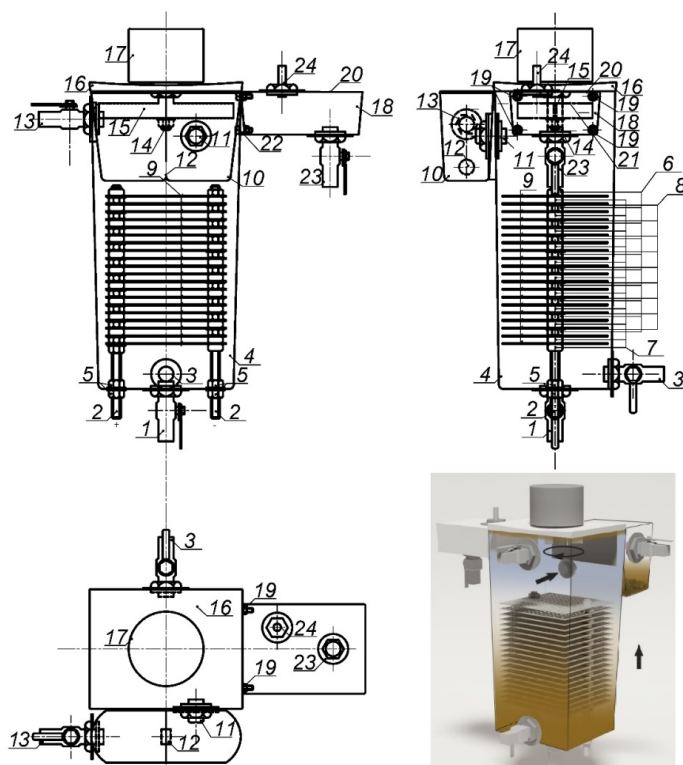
Электролизер-адсорбер для очистки СВ ТФ: 1 — кран для промывки устройства; 2 — направляющие контактные шпильки; 3 — штуцер подачи СВ; 4 — корпус устройства; 5 — гайки крепления контактных направляющих шпилек в корпусе установки; 6 — контактные гайки крепления пластин электродов; 7 — диэлектрические гайки крепления пластин электродов; 8 — диэлектрические прокладки; 9 — пластины электродов электролизера; 10 — адсорбер; 11 — штуцер для подачи в адсорбер СВ, прошедшей электрохимическую обработку; 12 — переливное отверстие адсорбера; 13 — кран слива очищенной воды; 14 — вал скребкового механизма; 15 — скребковый механизм выполненный в виде лопастной мешалки; 16 — крышка корпуса электролизера-адсорбера; 17 — редуктор скребкового механизма; 18 — приемник флотошлама; 19 — болты крепления к электролизеру-адсорберу приемника флотошлама; 20 — крышка приемника флотошлама; 21 — отверстие для подачи флотошлама в приемник флотошлама с помощью скребкового механизма, выполненного в виде лопастной мешалки, расположенной над поверхностью обрабатываемой жидкости; 22 — соединительная прокладка; 23 — кран для перекачки флотошлама; 24 — газотводный патрубок
